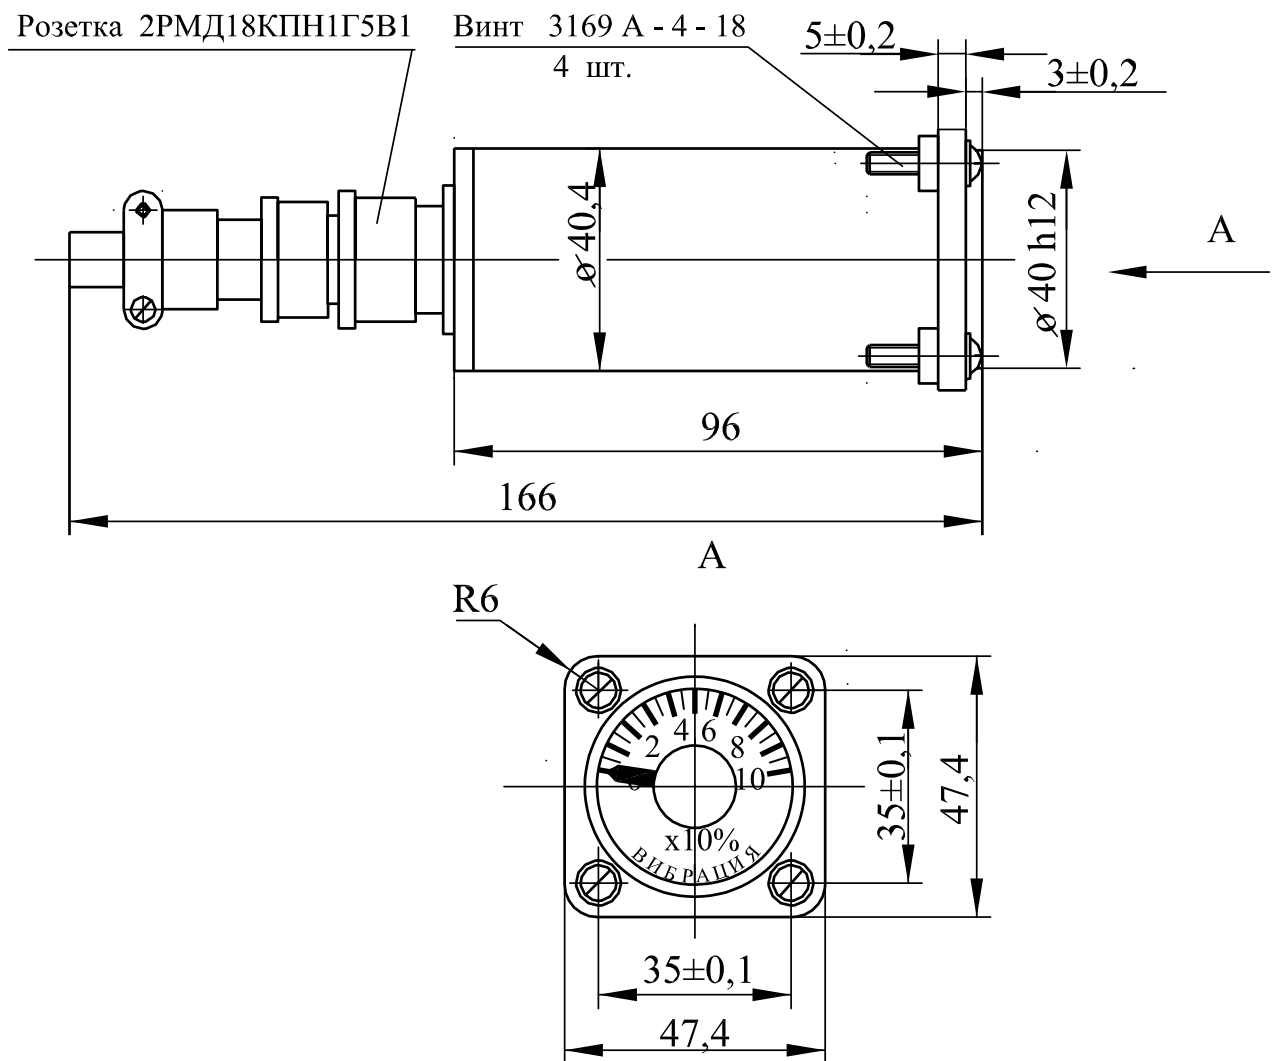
Габаритно-установочные размеры указателя УК-68В
